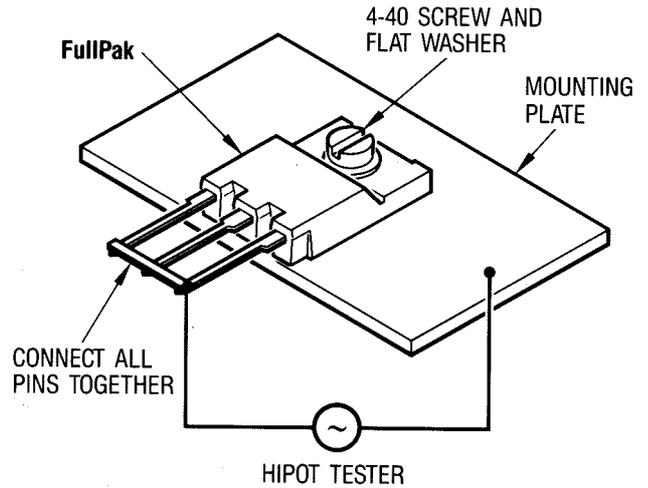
Типовое крепление корпуса FullPak на держатель тестера Hipot
